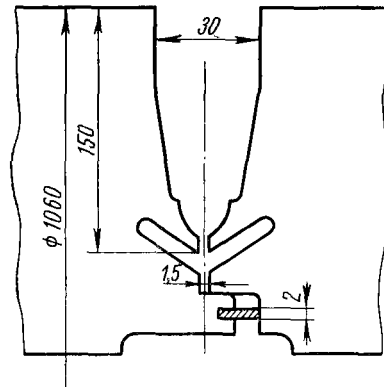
Конструкция стыка кольцевого соединения вала ротора турбины
